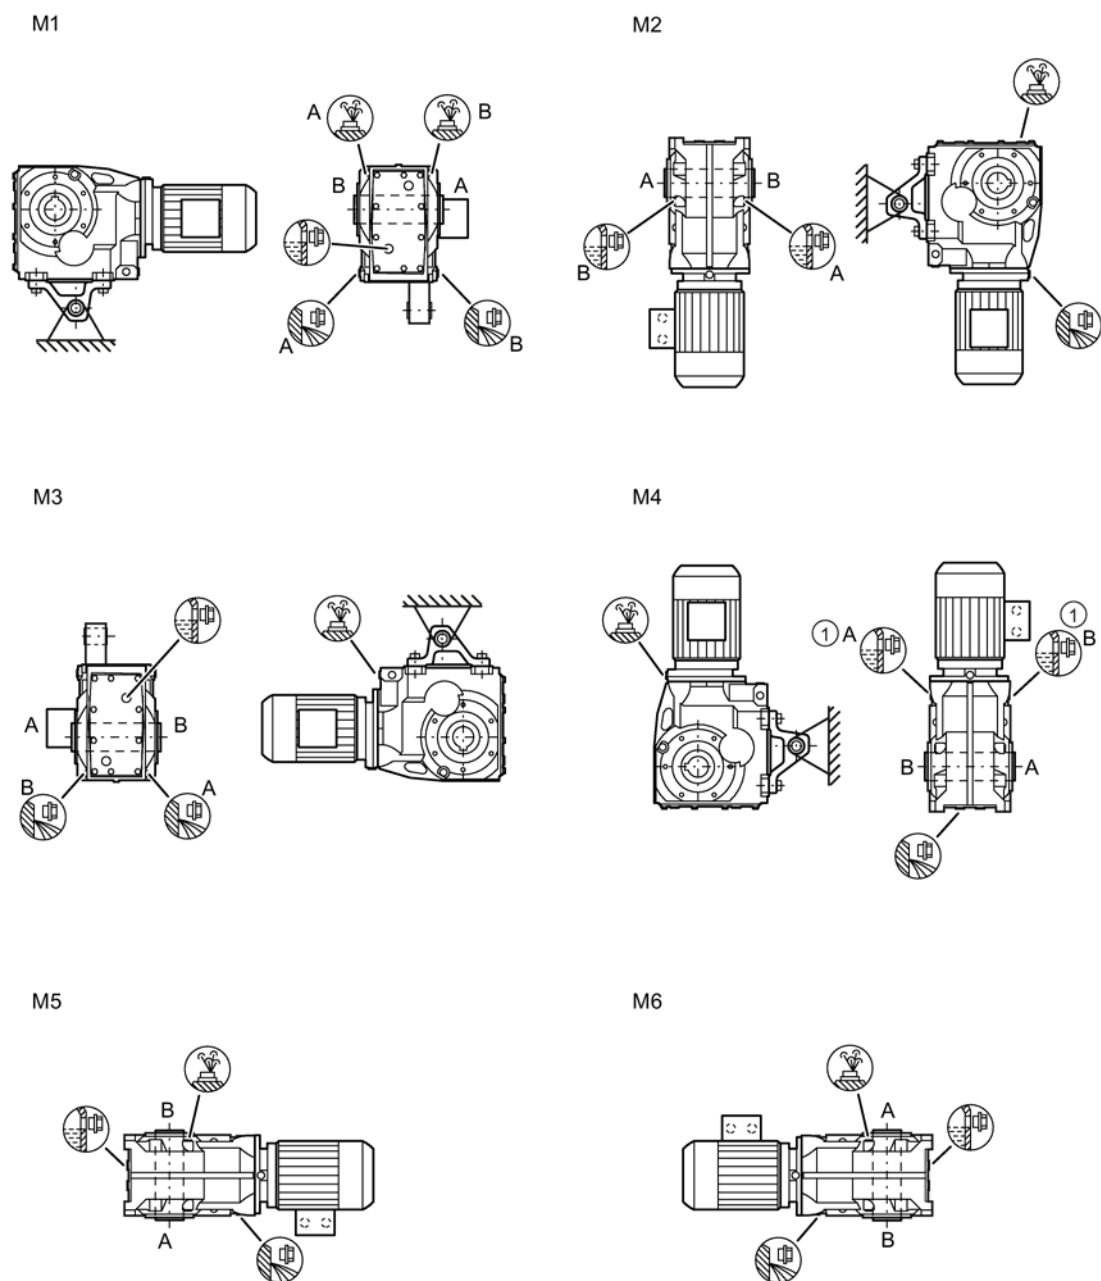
Монтажные положения для конического редуктора KAD в насадном исполнении, типоразмеры 39-189
